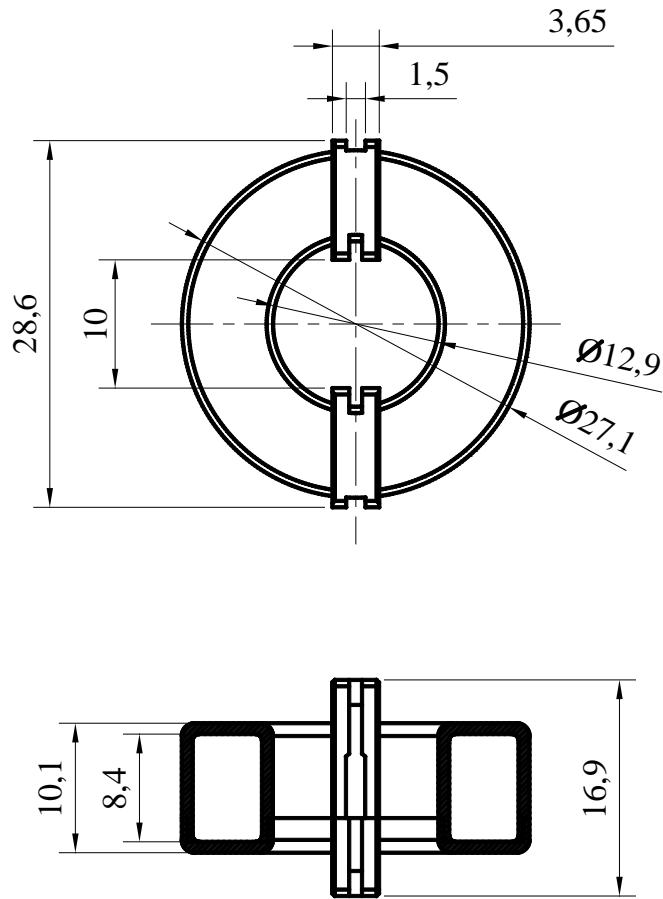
Внешний вид и габаритные размеры магнитопровода MSFN-25D-TH1
